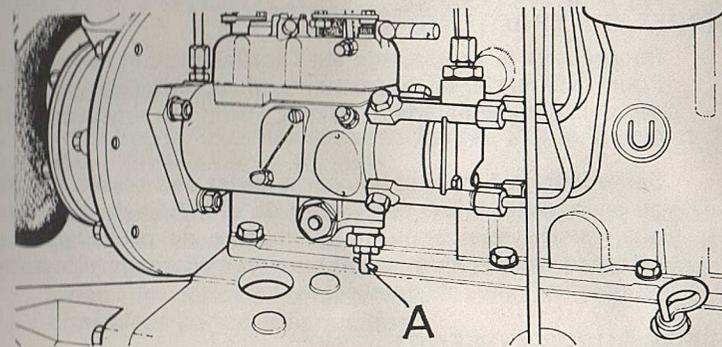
/11. POMPE A INJECTION DE CARBURANT
